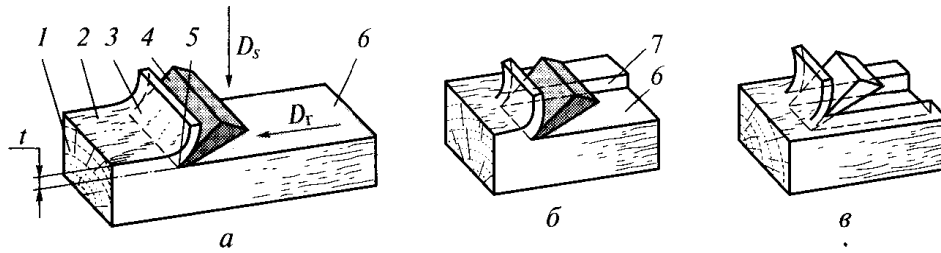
Схеми різання: а – відкрите; б – напівзакрите; в – закрите; 1 – заготовка; 2 – оброблювана поверхня; 3 – стружка; 4 – різець; 5 – ріжуча крайка; 6 – поверхня різання; 7 – бічна поверхня різання
